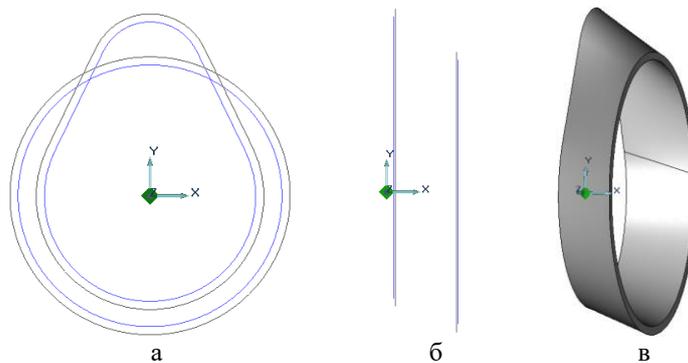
Построение модели боковой стенки среднего корпуса
